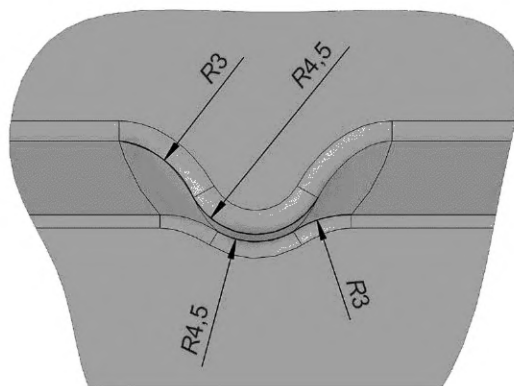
Форма и размеры выемки (деталь X), приведенной на рисунках 6 и 7
